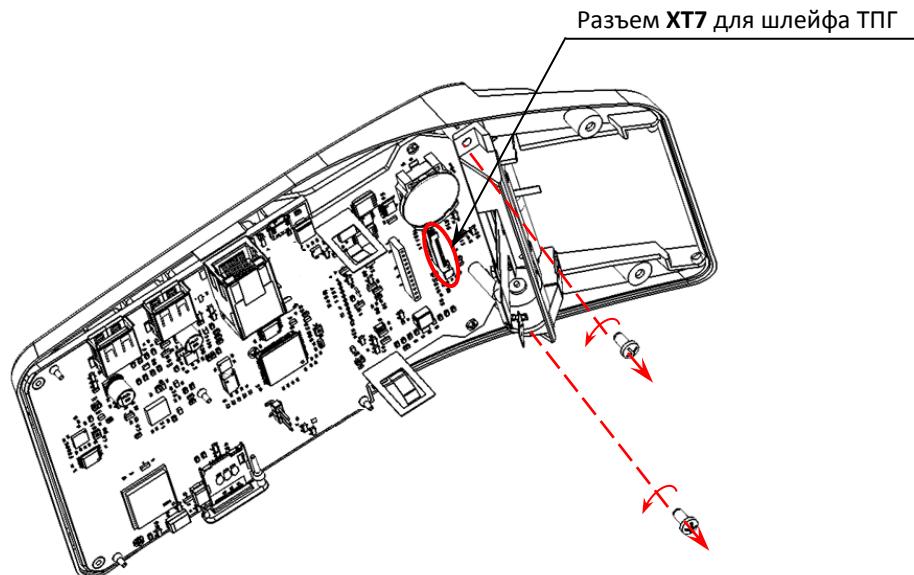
Винты крепления ТПГ к верхней части корпуса
